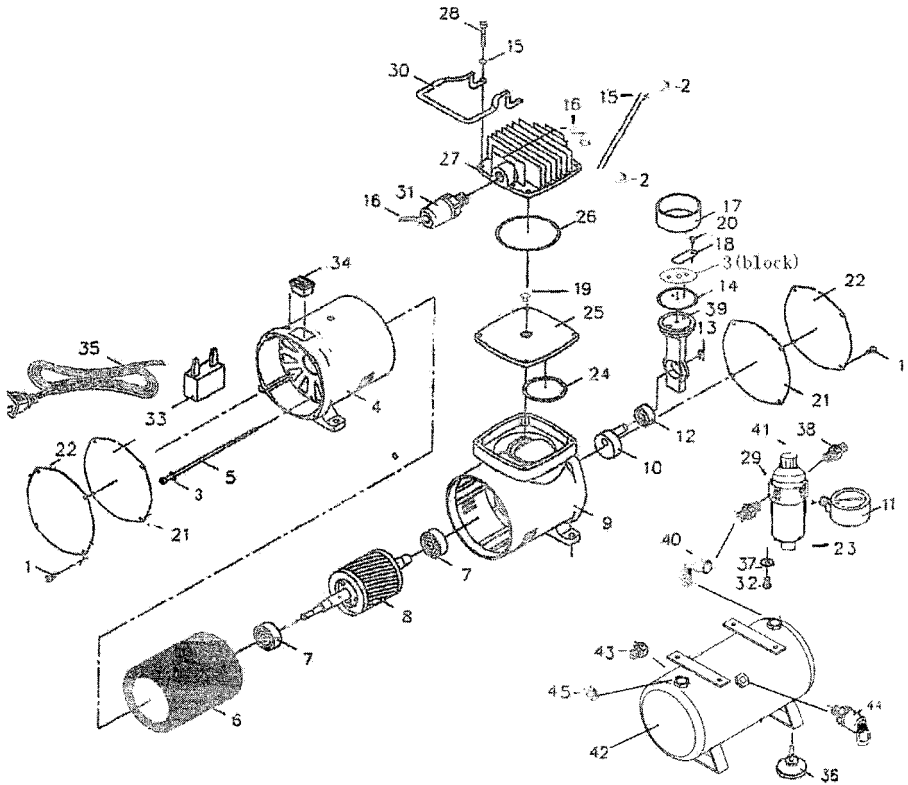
Схема компрессора 81-125 | Мал. 3. Схема компрессора 81-125 | Fig 3. Layout of compressor 81-125
